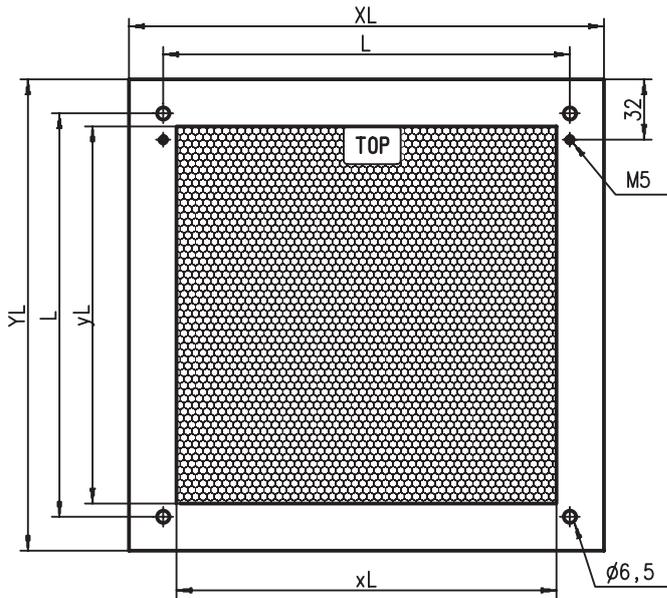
Maßzeichnung Reflexfolie auf Trägerplatte
